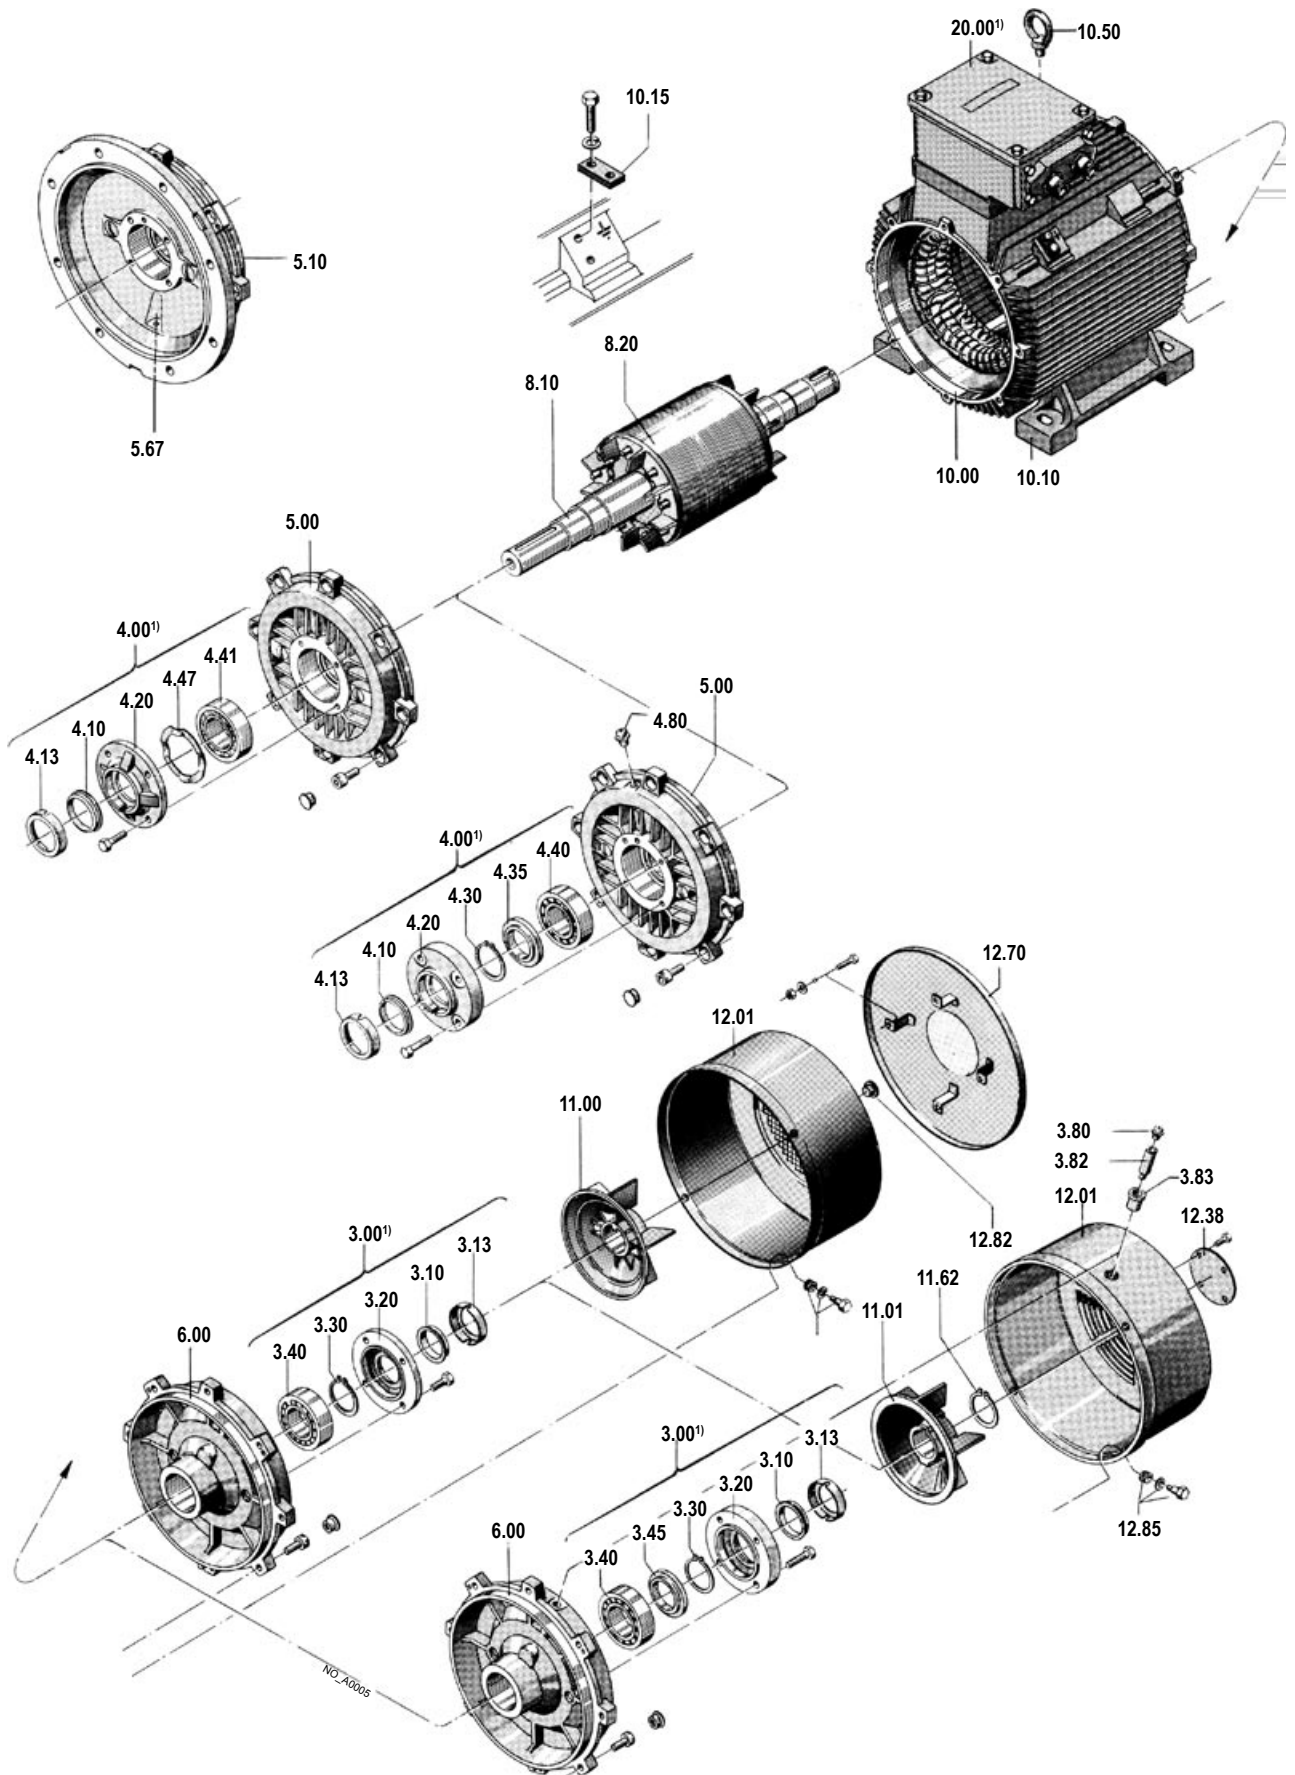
a: Drehstrommotor, Grundausführung 1MJ7 (Beispiel, gelieferte Ausführung kann in Details abweichen)
